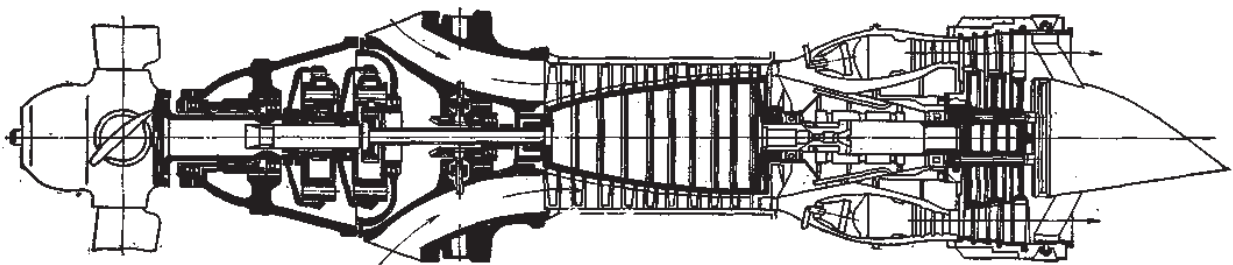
Однороторный ТВД с присоединенным редуктором для привода одиночного воздушного винта
